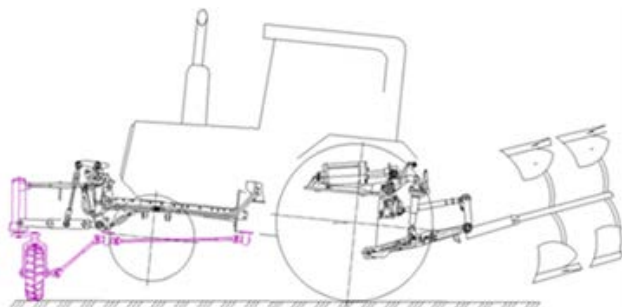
Опорно-маневерное устройство и схема его присоединения к двигателю
